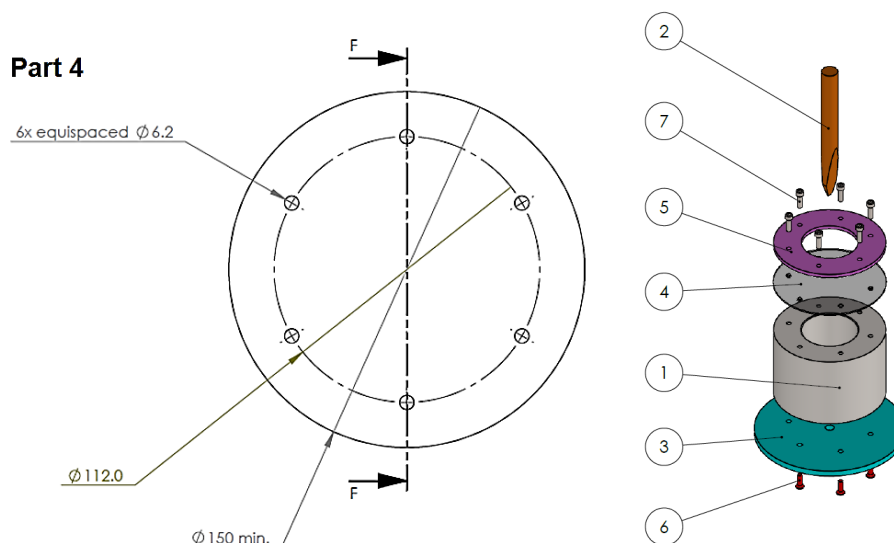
Échantillon de réservoir de carburant et assemblage général
